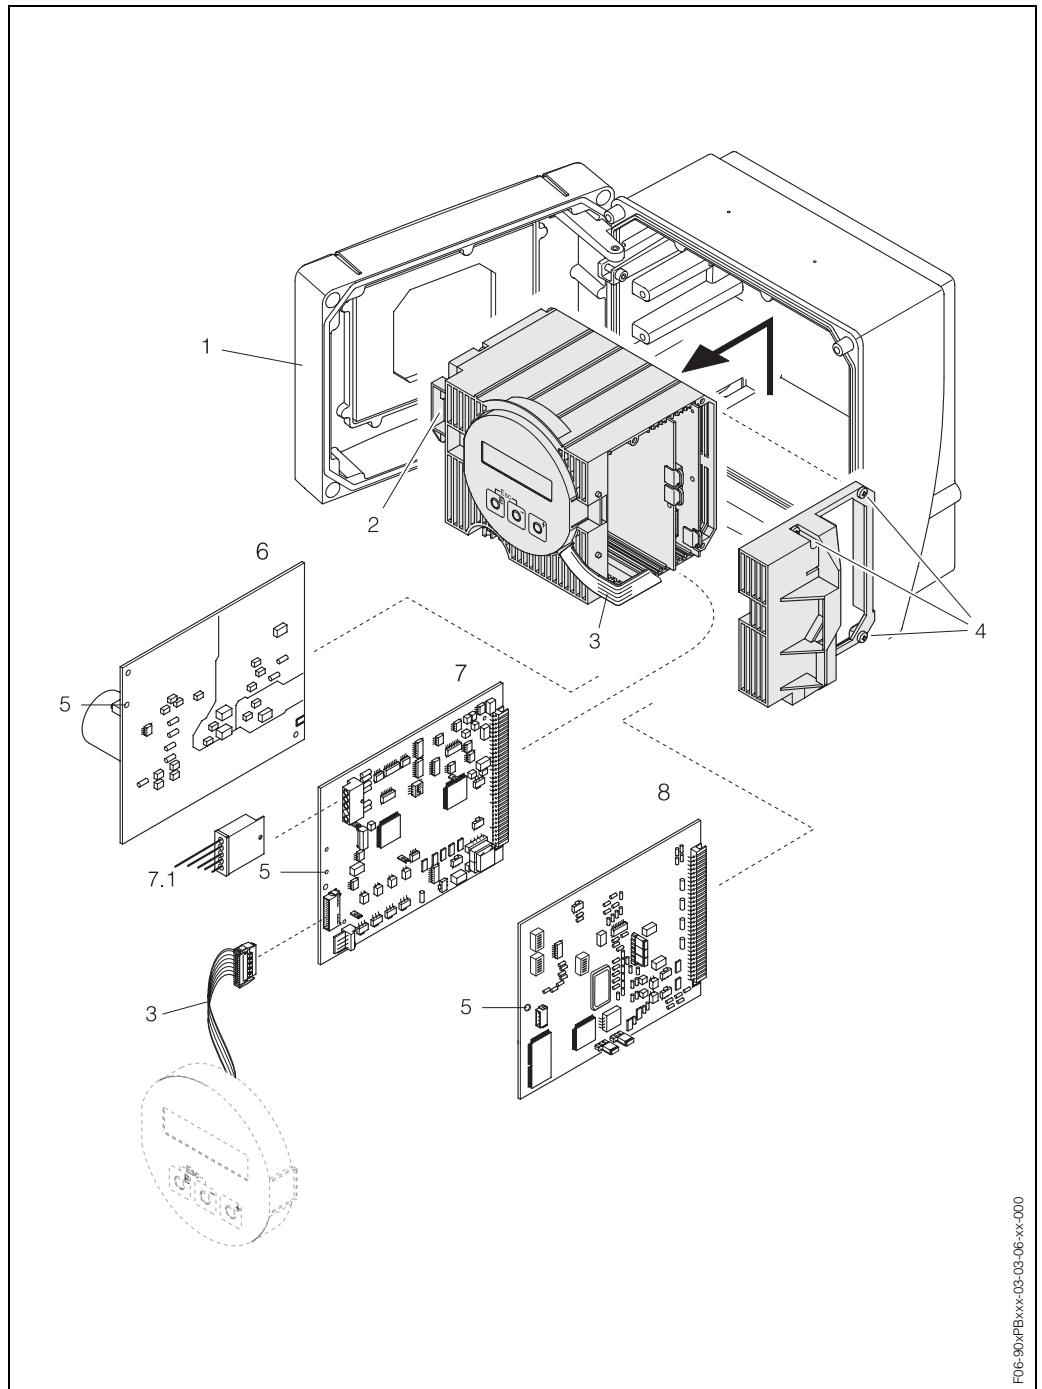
Caja de montaje mural: desmontaje e instalación de las placas de la electrónica
